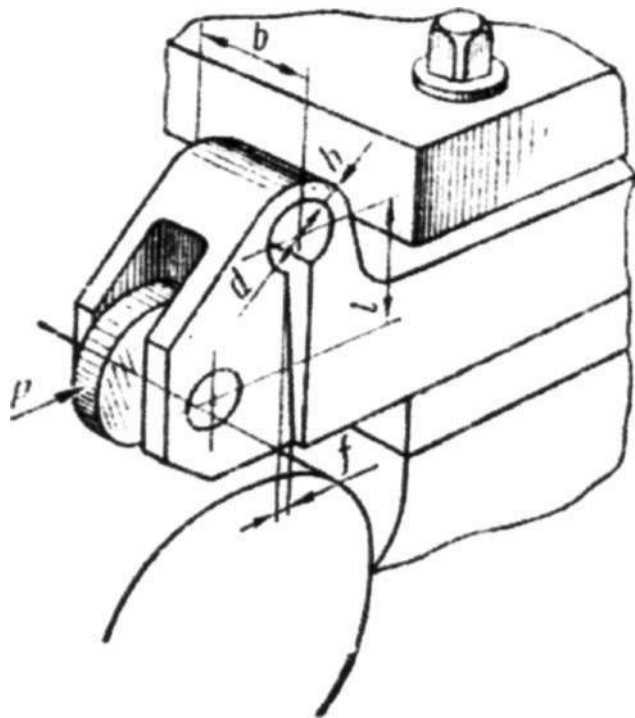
Универсальное однороликовое устройство с пружинящим корпусом
